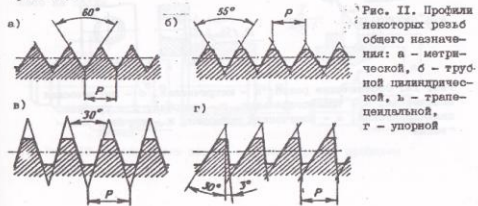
Профили некоторых резьб общего назначения: а - метрической, б - крупной цилиндрической, в - треугольной, г - упорной
